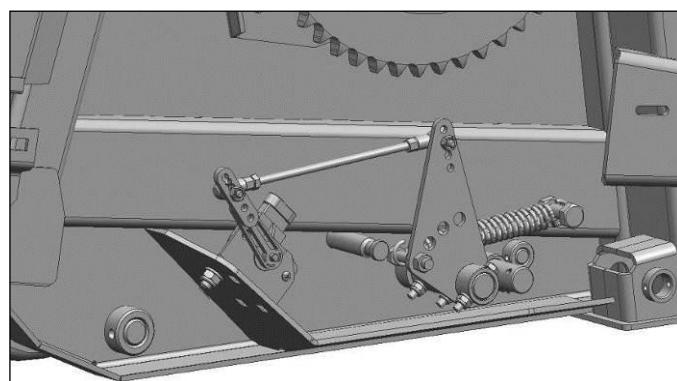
Положение датчиков для уборки сои в режиме «с плавающим ножом» с правой стороны жатки
